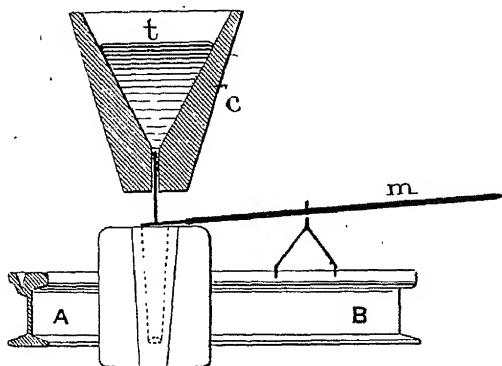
Soudure des rails par l'aluminothermie : schéma du dispositif.
